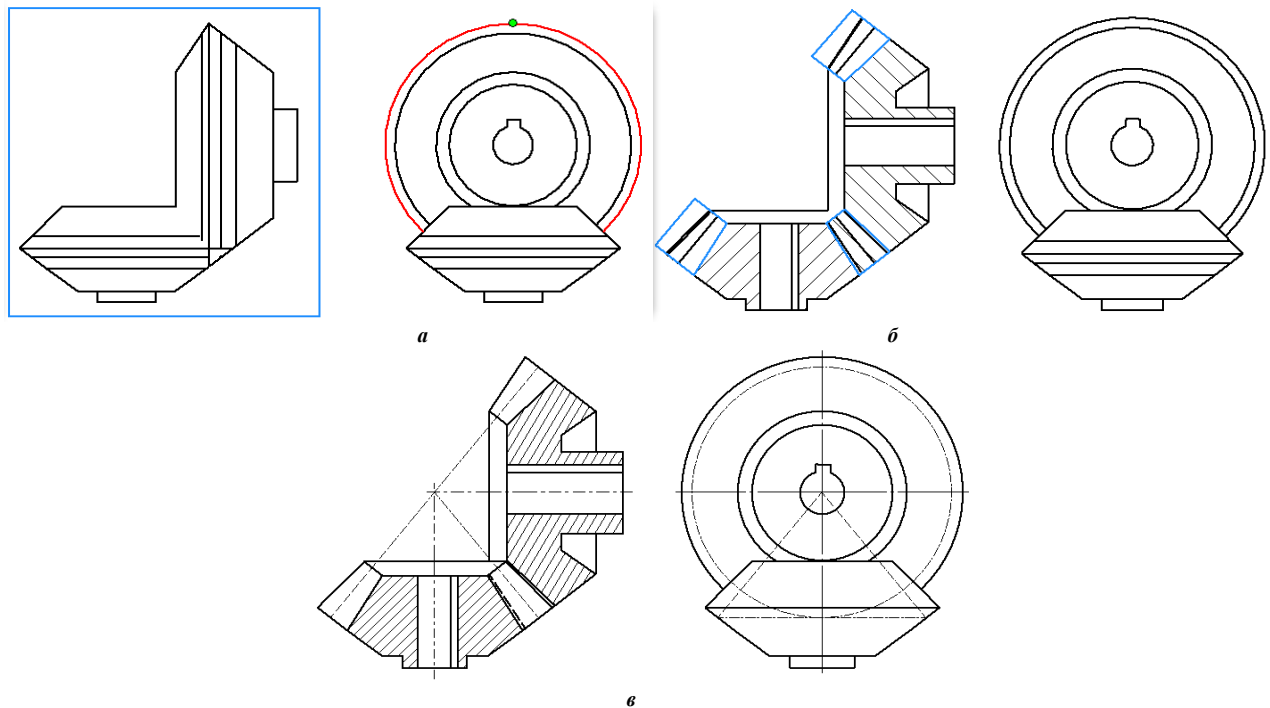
Передачі зачепленням: а – 1-й місцевий розріз; б – 2-й місцевий розріз; в – фрагмент кресленника конічної зубчастої передачі
